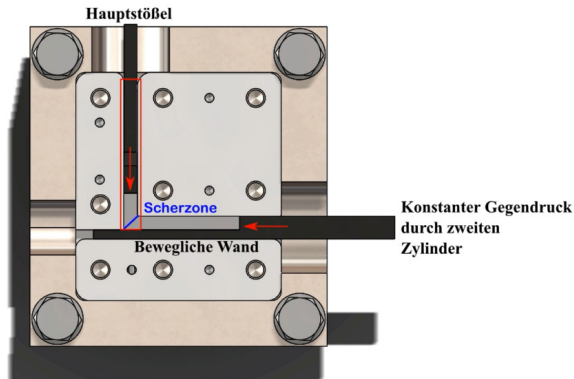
Schnittansicht des entwickelten ECAP Werkzeuges
